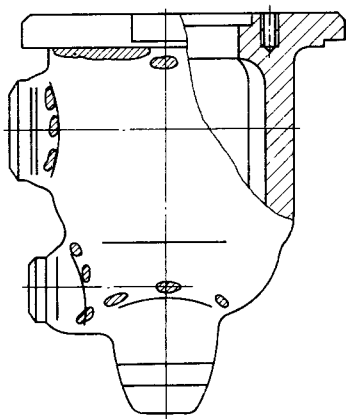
Места появления трещин в корпусе стопорного клапана
